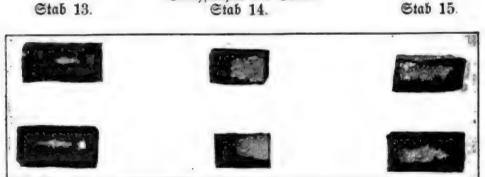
Bruchflächen der Stäbe. Stab 13. Stab 14.
